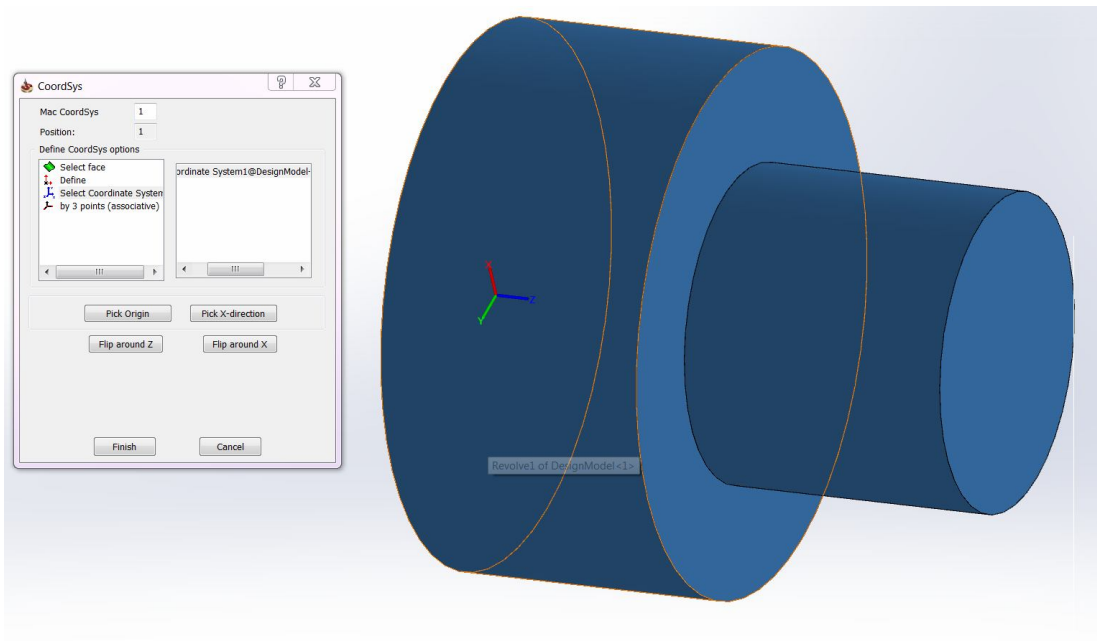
Вибір розташування початку системи координат деталі
